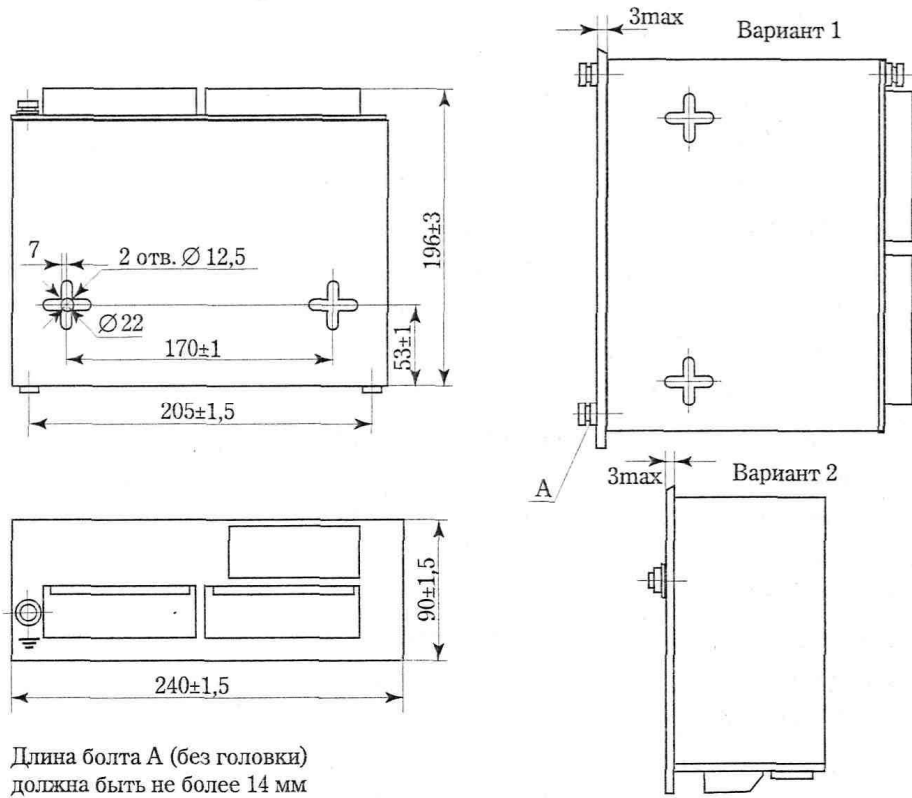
Габаритные и установочные размеры ПБР-3 и ПБР-3А
